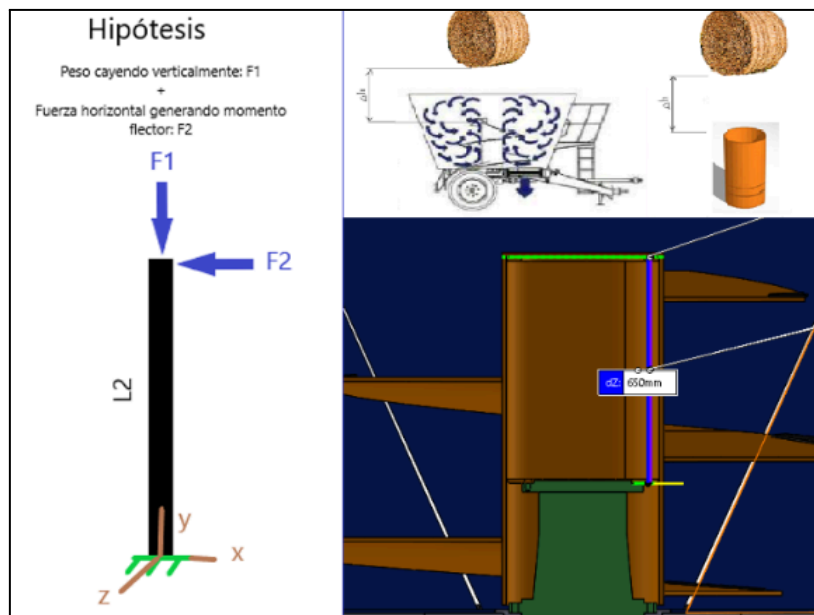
Hipótesis de fuerzas aplicadas sobre el sinfín
